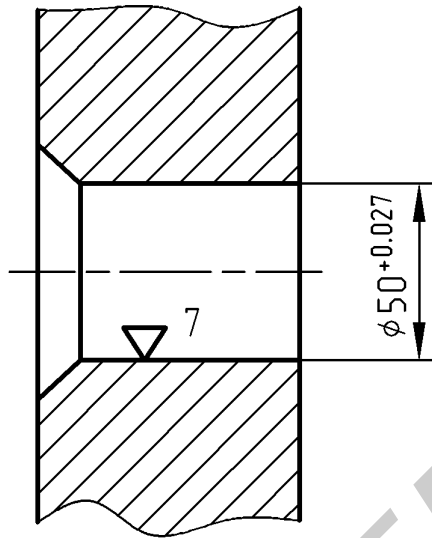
Фрагмент детали с обрабатываемым отверстием
